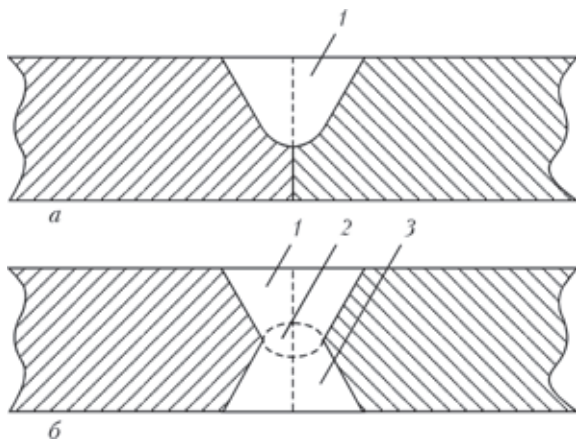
Схематическое изображение этапов формирования двухстороннего стыкового соединения лазерной сваркой: *а* — лазерная дорожка с одной стороны; *б* — наложение лазерной дорожки со второй стороны (1 — шов 1; 2 — корень шва; 3 — шов 2)
